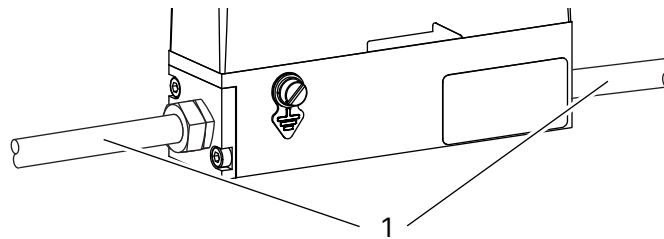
Medienanschlüsse, z. B. Innengewindeanschlüsse
